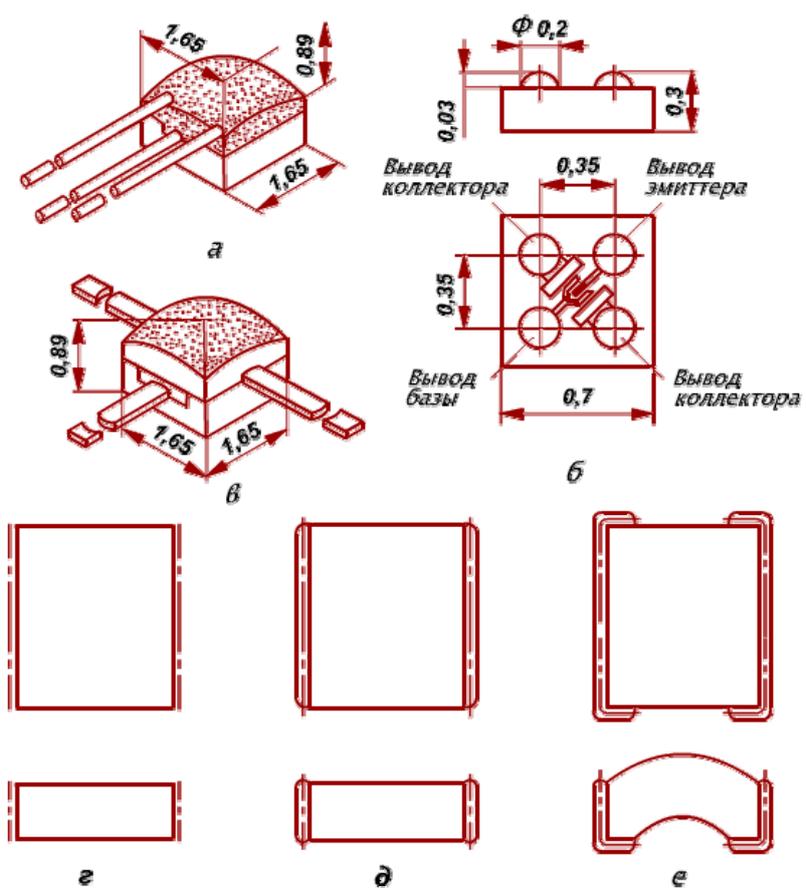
Бескорпусный транзистор с гибкими (а), шариковыми (б) и балочными (в) выводами; нелуженый (z) и луженый (д, е) бескорпусные конденсаторы
